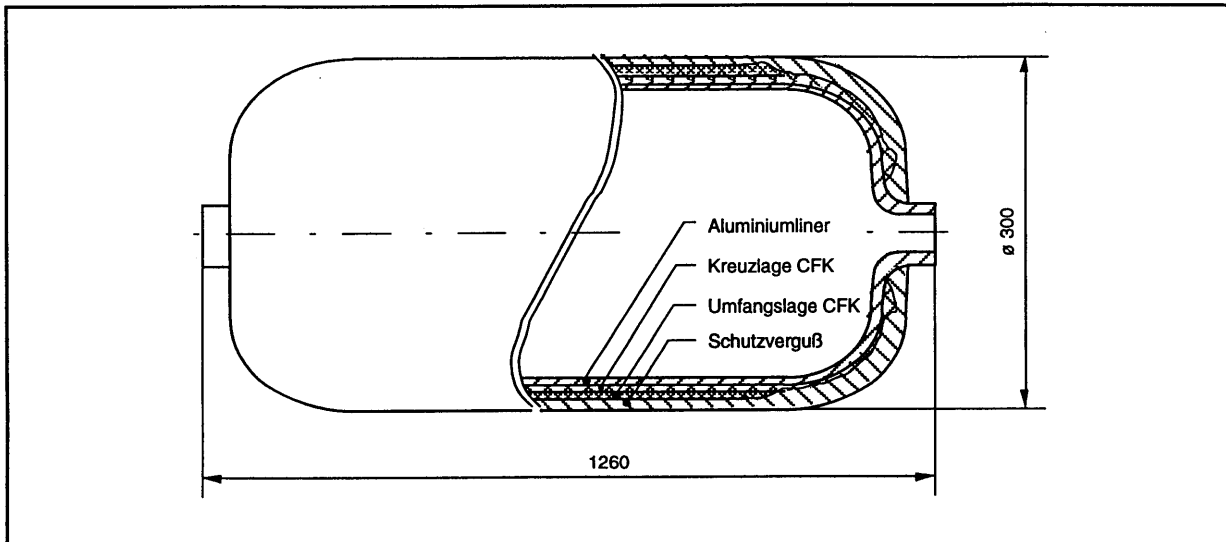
Schnitt durch einen Druckbehälter mit Aluminium-Liner (Quelle: IVW)
